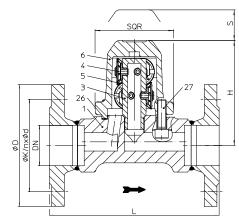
1....6K2 (DN40-50) com 6 cápsulas, com flanges
